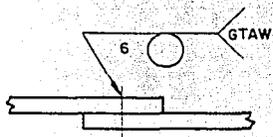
APLICACION DE SIMBOLO DE SOLDADURA DE FUSION
